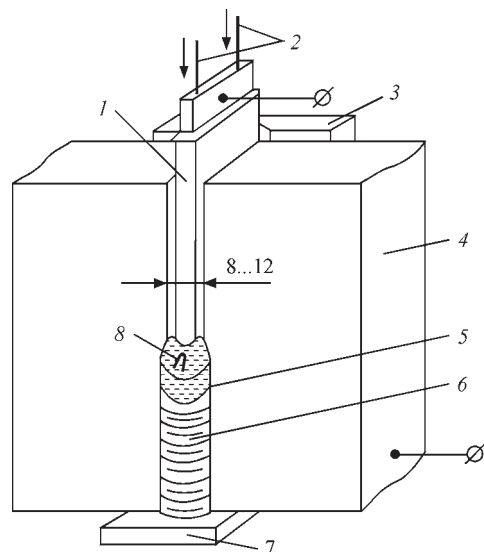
Схема електродугового зварювання закладним електродом: 1 – закладний електрод; 2 – присадний дріт; 3 – формуючі накладки; 4 – зварюваний виріб; 5 – зварювальна ванна; 6 – зварний шов; 7 – підкладка; 8 – дуга
